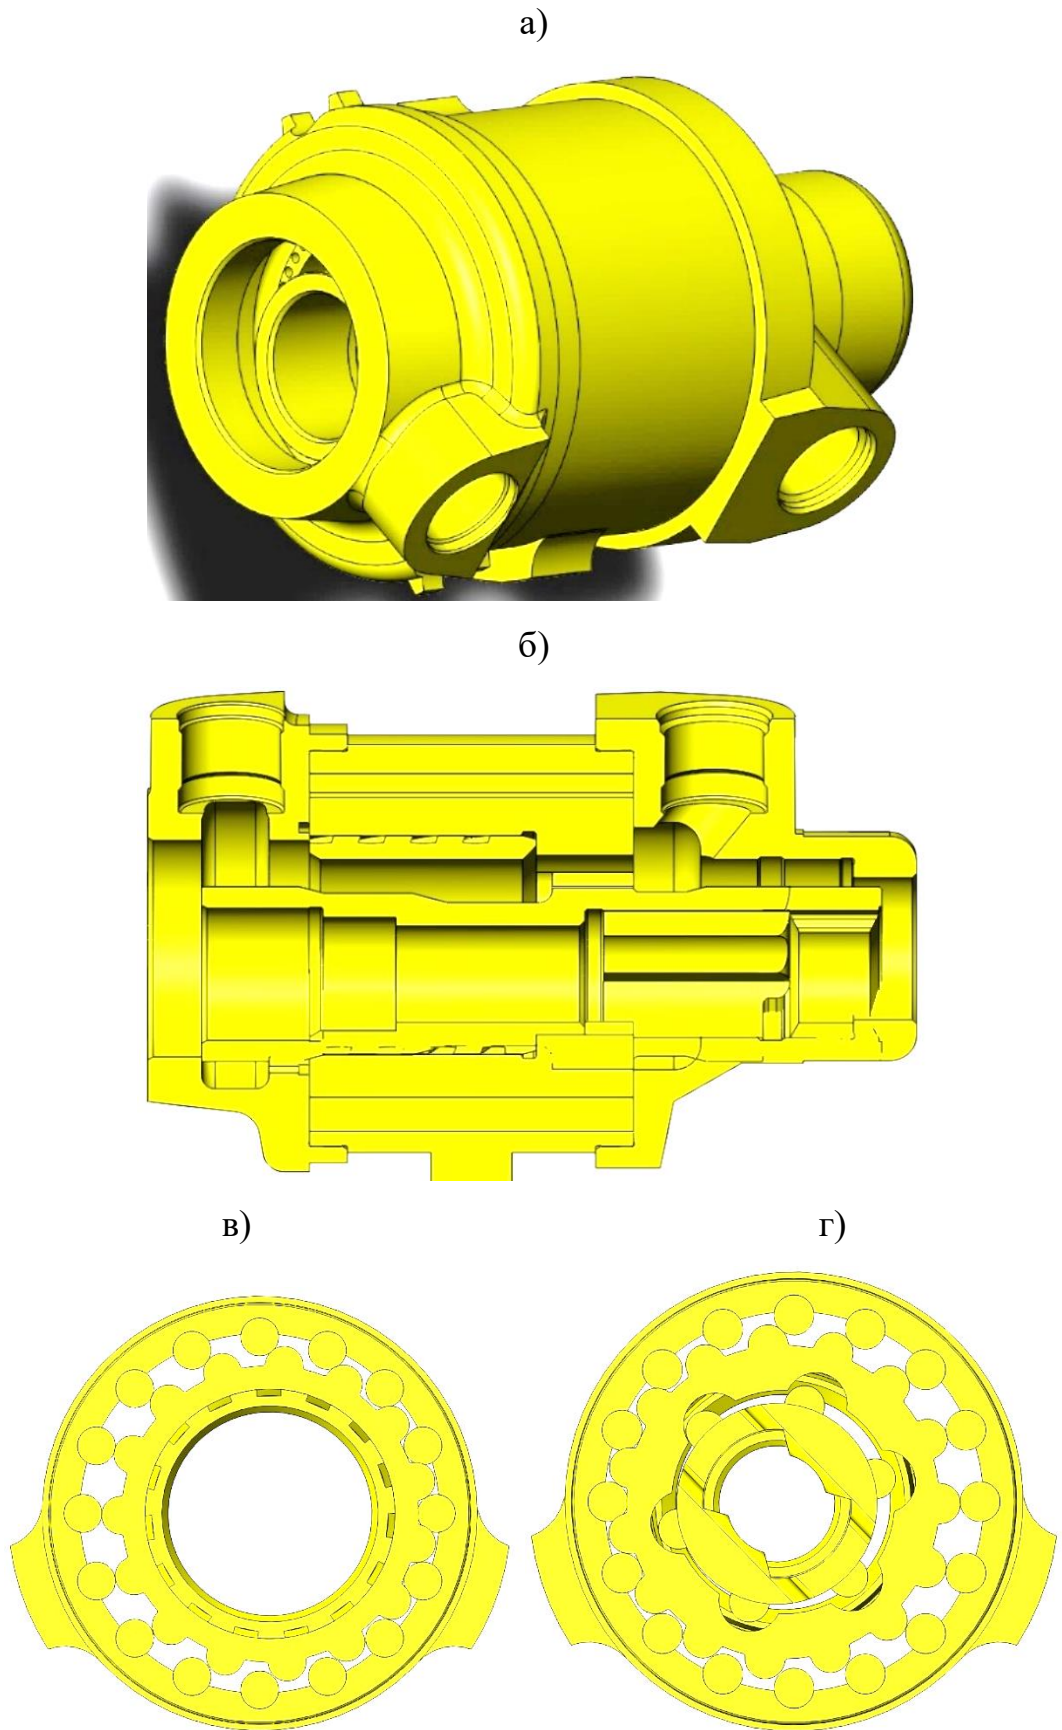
конструкція механізму обертання бурової штанги колонкового перфоратора ПК-60: а – загальний вид, б – переріз повздовжній, в – переріз без
